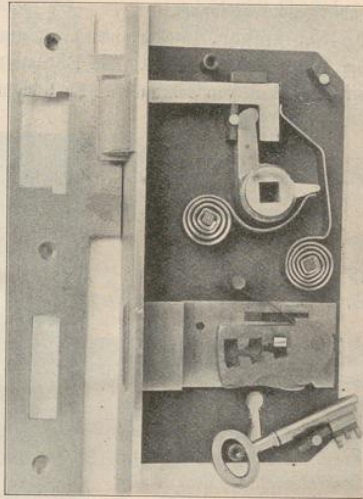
Zweitouriges eingestecktes Chubb'sches Schlofs mit vier Messingzuhaltungen; Schlüssel unten querliegend.
